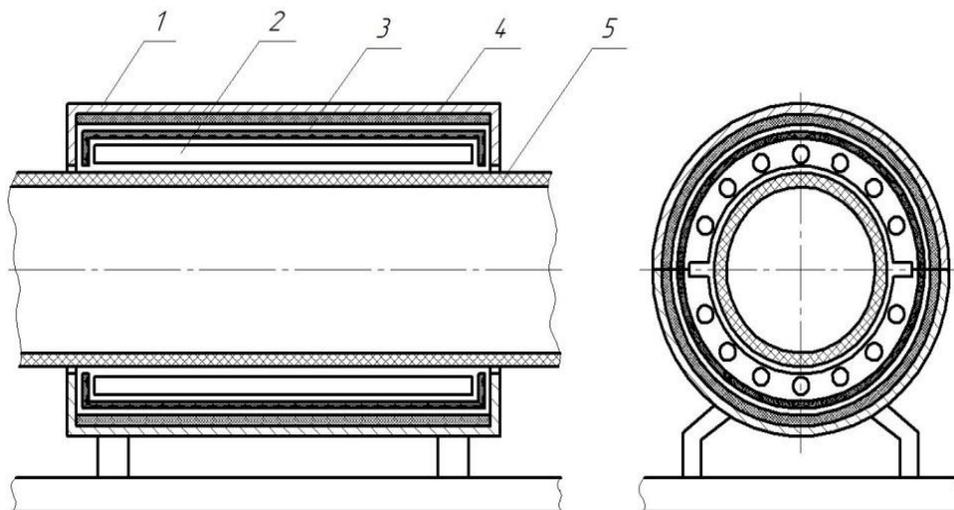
Установка для текущего ремонта напорного пожарного рукава:
